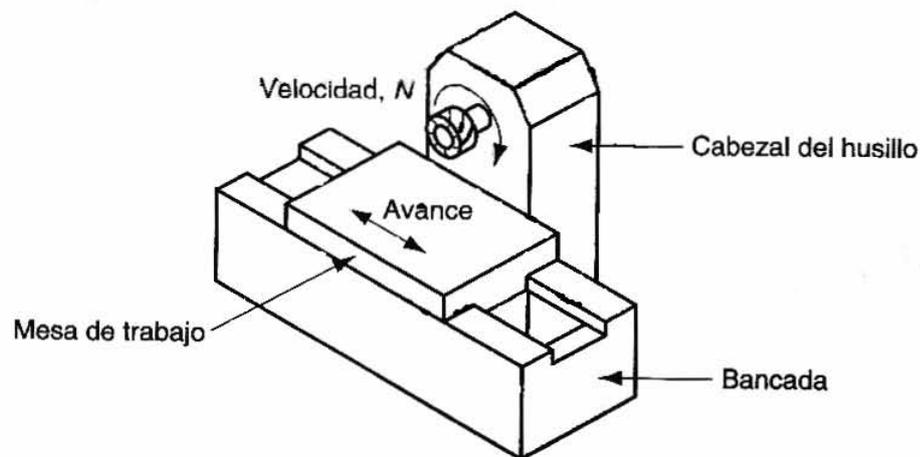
Fresadora tipo cama simplex de husillo horizontal.
